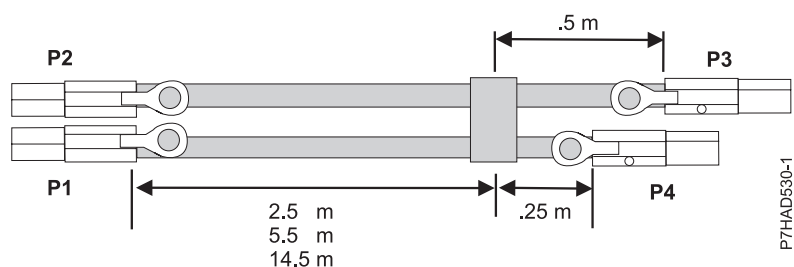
Comprimentos de cabos de montagem de cabo X externo SAS
